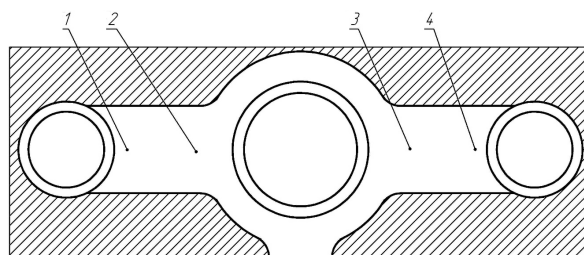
Схема патрубков перед регулирующими клапанами (сечение В-В, рис. 1), точками 1–4 обозначены места контроля напряжений
